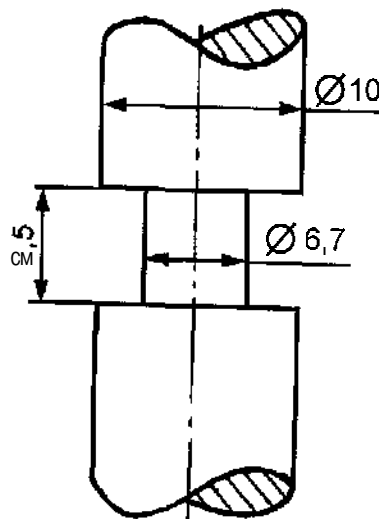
Размеры канавки под резиновое уплотнительное кольцо
